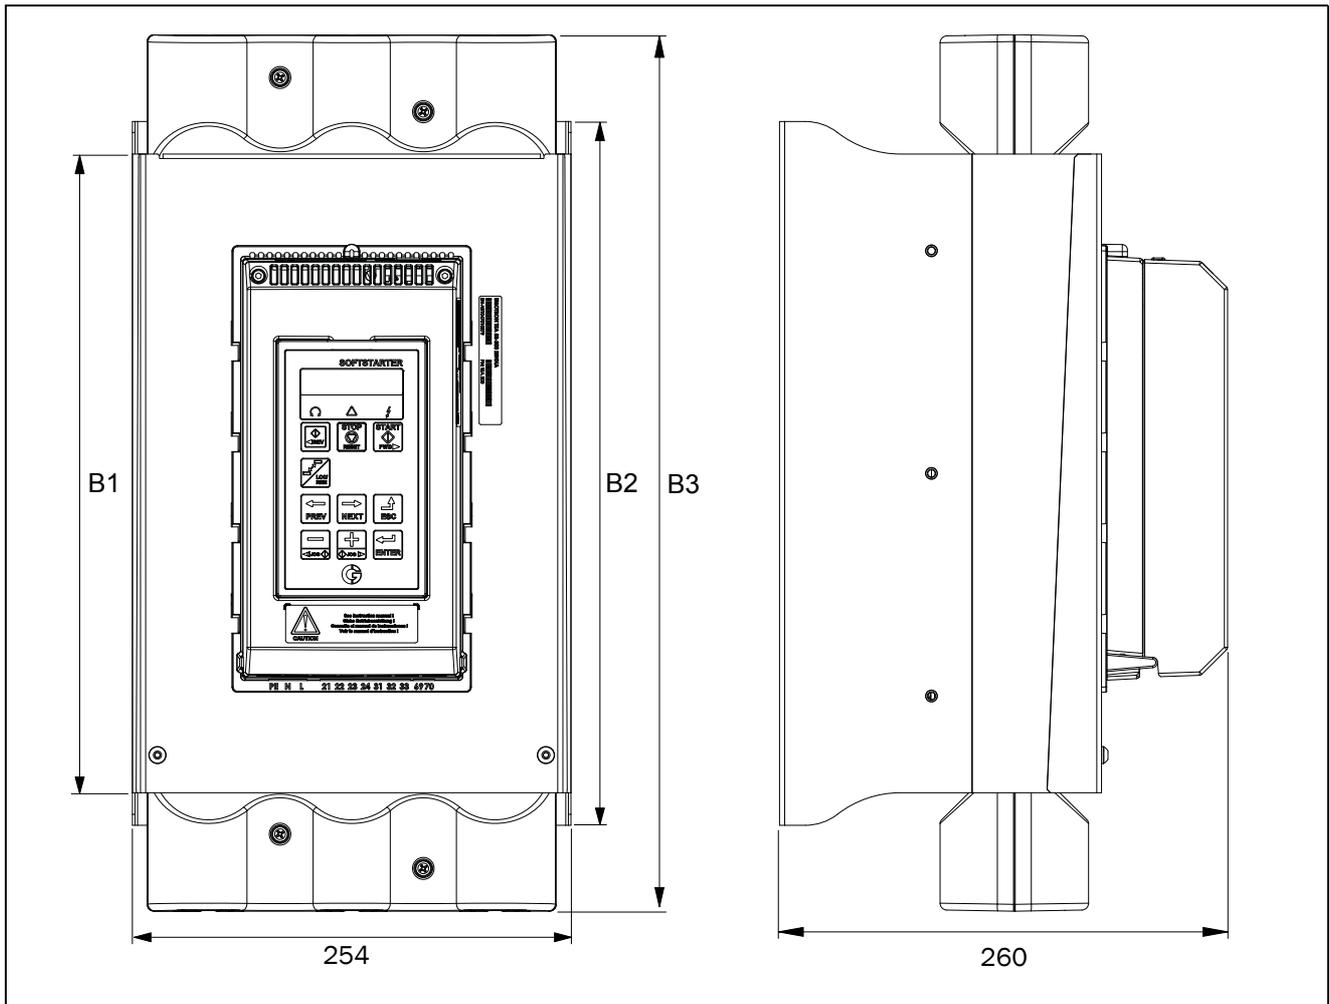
Габаритные размеры Emotron TSA типоразмера 4.
